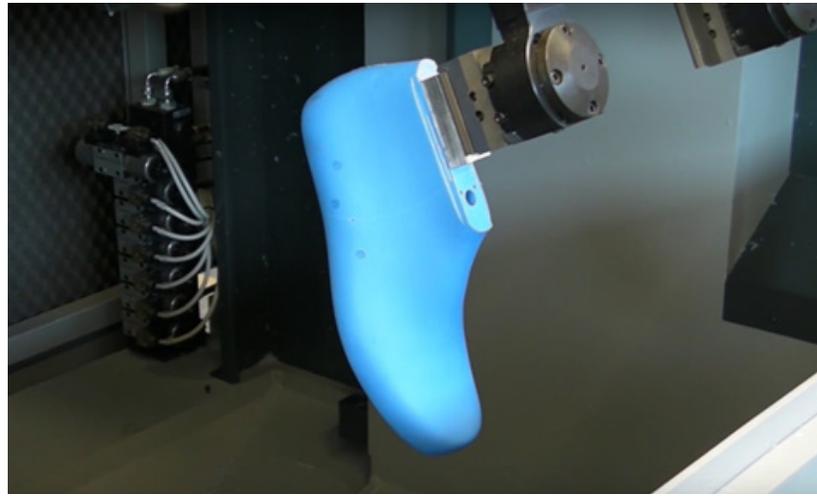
Horma de plástico moldeado (Newlast Group, 2017).
